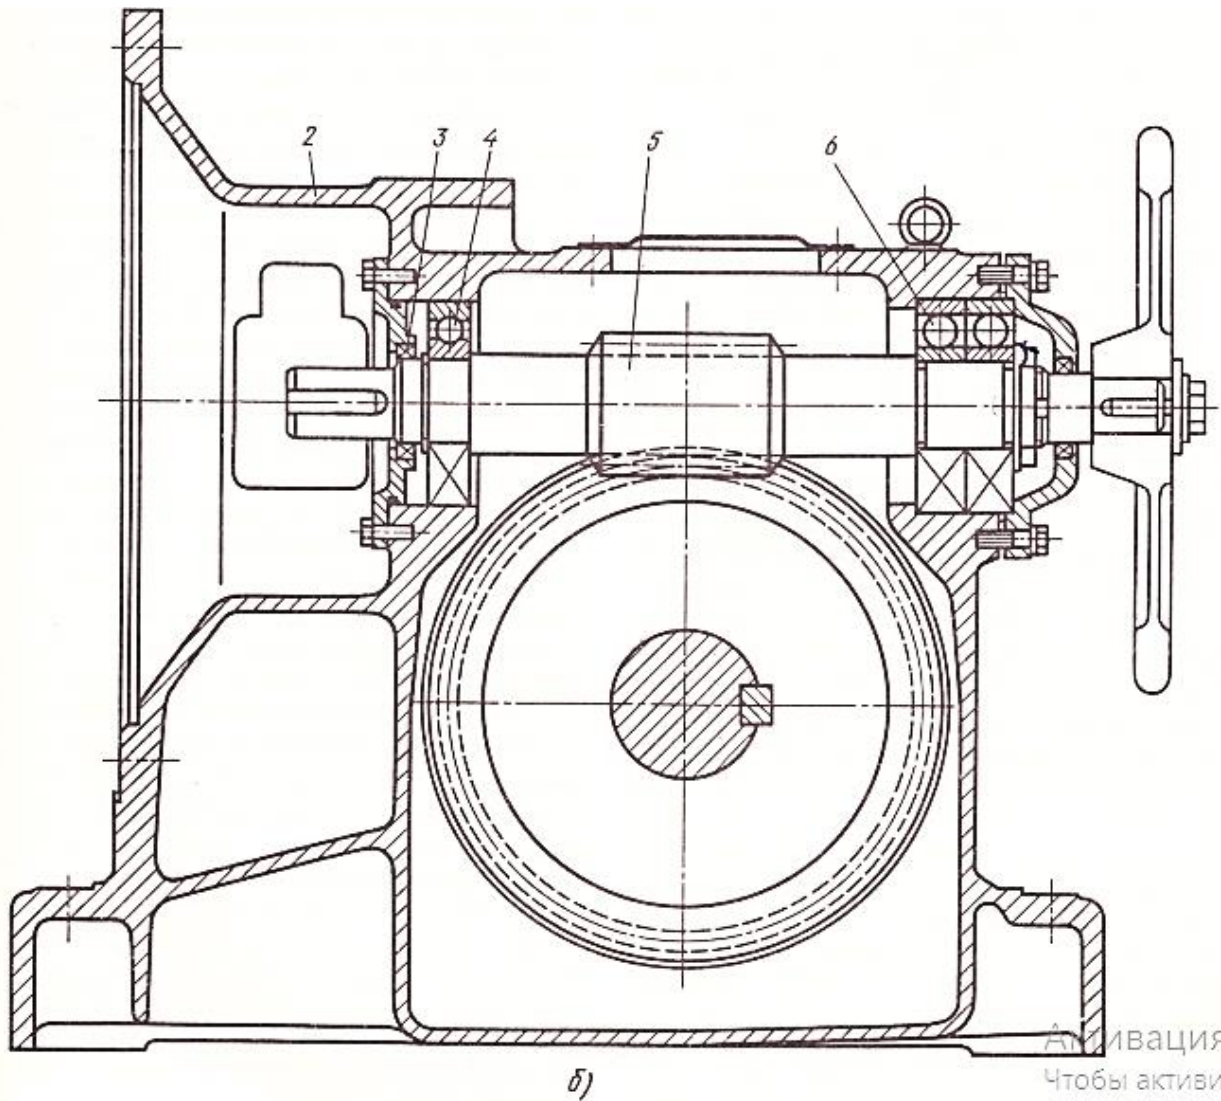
Червячный редуктор с консольным расположением канатоведущего шкива
